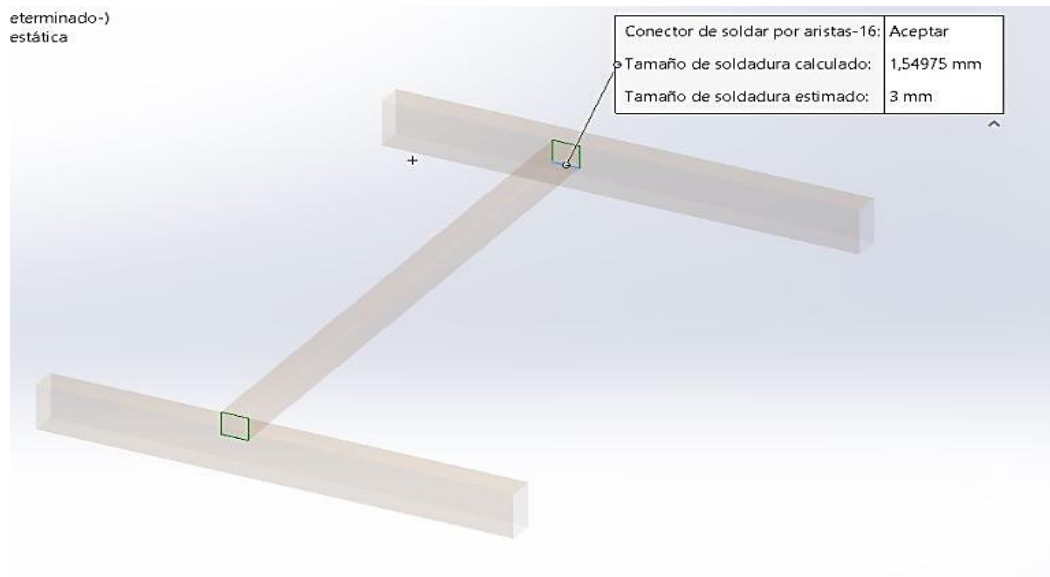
Tamaño de soldadura en uno de los conectores.
